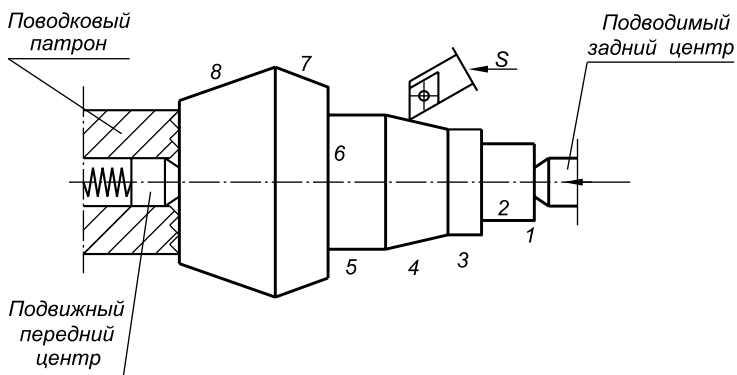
Последовательная концентрация операций токарной обработки заготовки под коническую шестерню на станке с ЧПУ: 1—8 — последовательно обрабатываемые поверхности заготовки;  $S$  — подача инструмента
